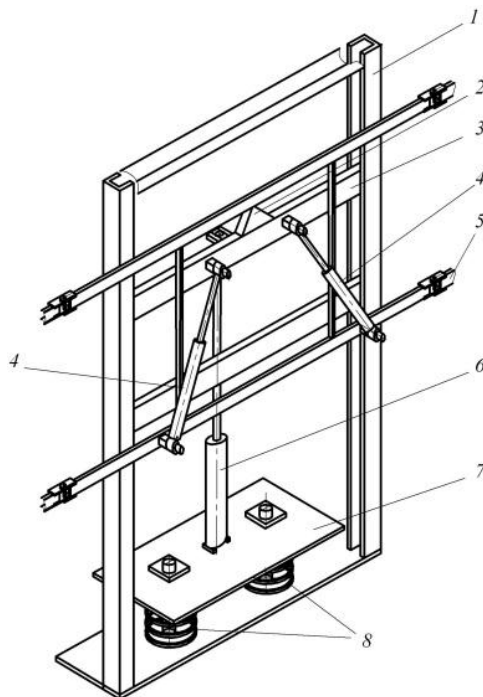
Схема установки штанги на раме полевого опрыскивателя
